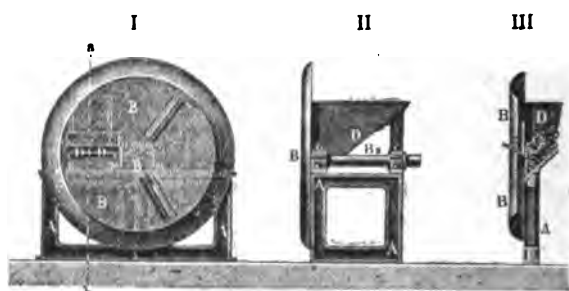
Machine à découper la gutta-percha brute (Système Hancock).
